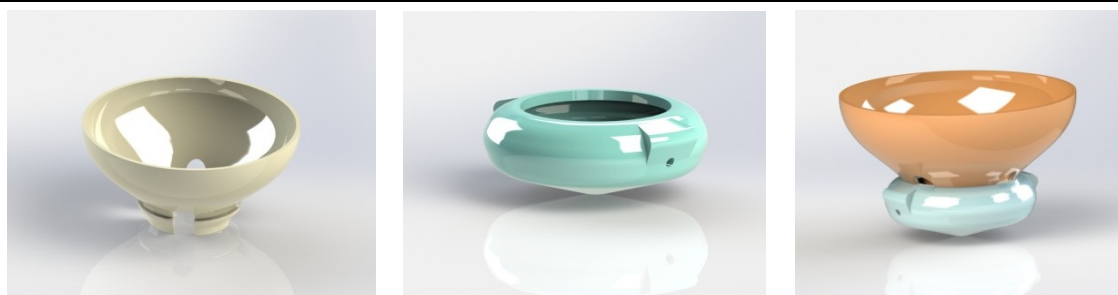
Modelagem 3D do conjunto funil e boca dispensadora
